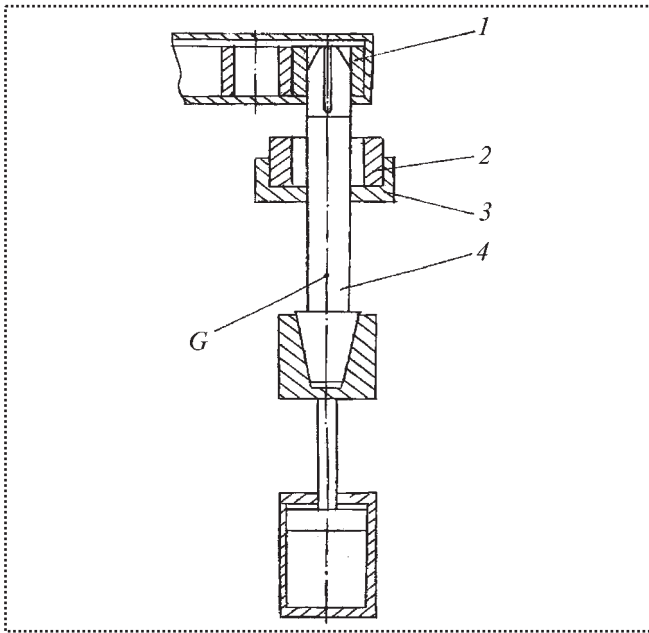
Схема сборки с помощью смещения центра тяжести детали
